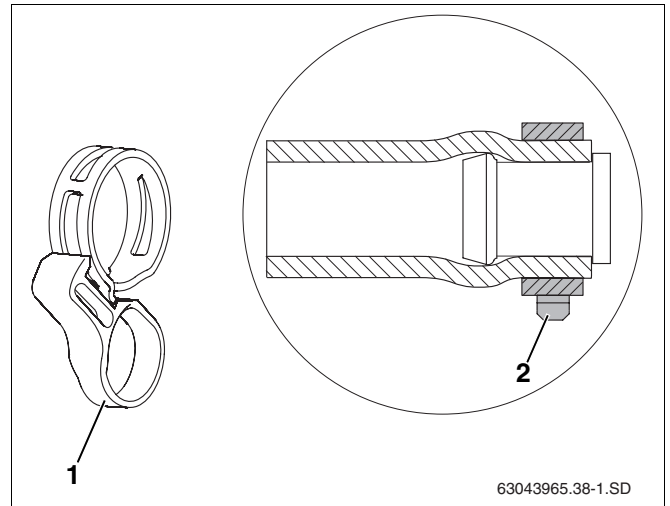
Braçadeira de mola com anel de fixação e no estado montado no tampão cego pré-montado
